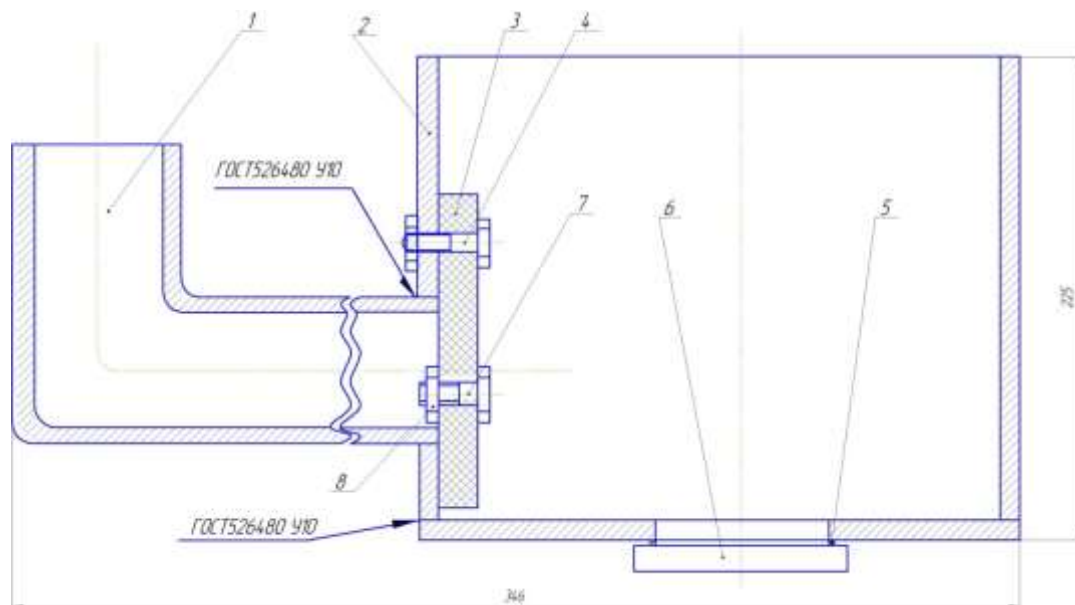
Конструктивна схема напувалки: 1 – з'єднувальна трубка; 2 – чаша; 3 – клапан; 4 – болтове з'єднання М6; 5 – ущільнення; 6 – заглушка; 7, 8 – болтове з'єднання М8.
